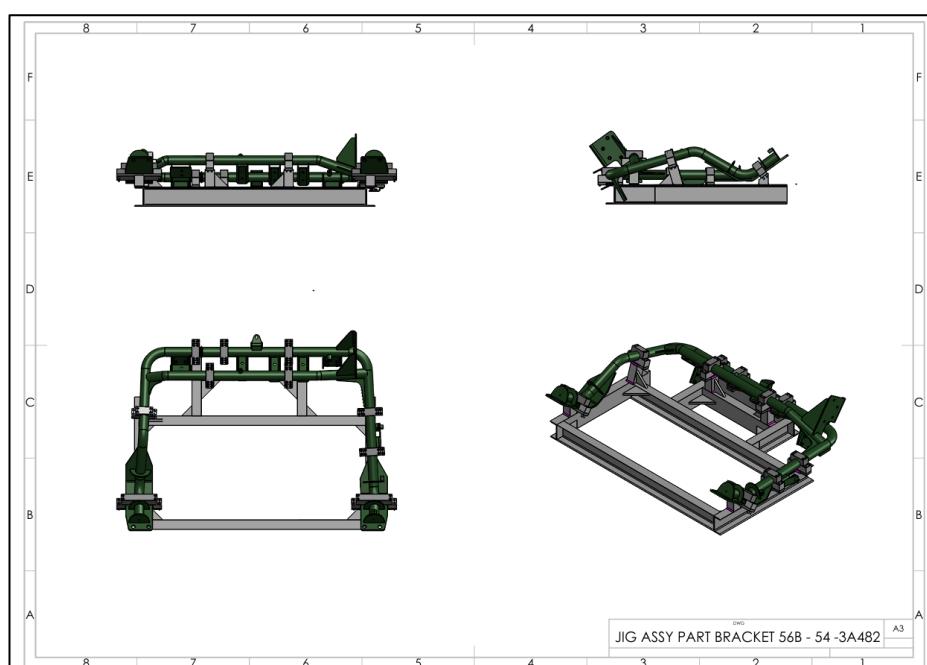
Desain 2D *Clamp Jig welding
